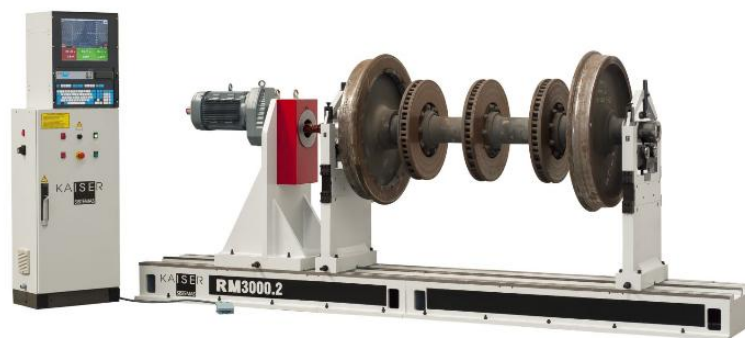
Máquina de equilibrar horizontal KAISER, com desmultiplicador na transmissão [30].
